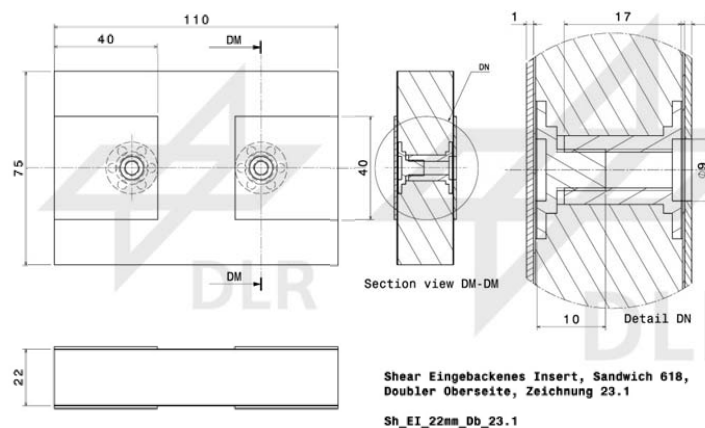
Dimensionen der 618 HC-Sandwichprobekörper inkl. integrierten Inserts (Schraubkonzept) für Shear-Versuche (Beispiel mit beidseitiger Deckschichtverstärkung)
